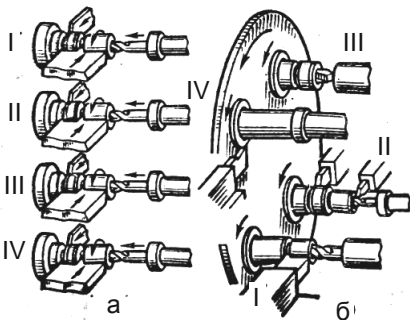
Схеми багатошпindelної токарної обробки
